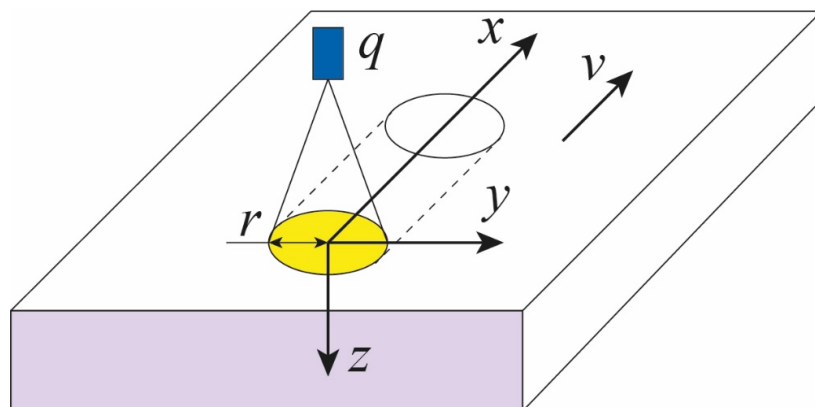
Процесс движения лазерного луча при нагреве стальной заготовки
